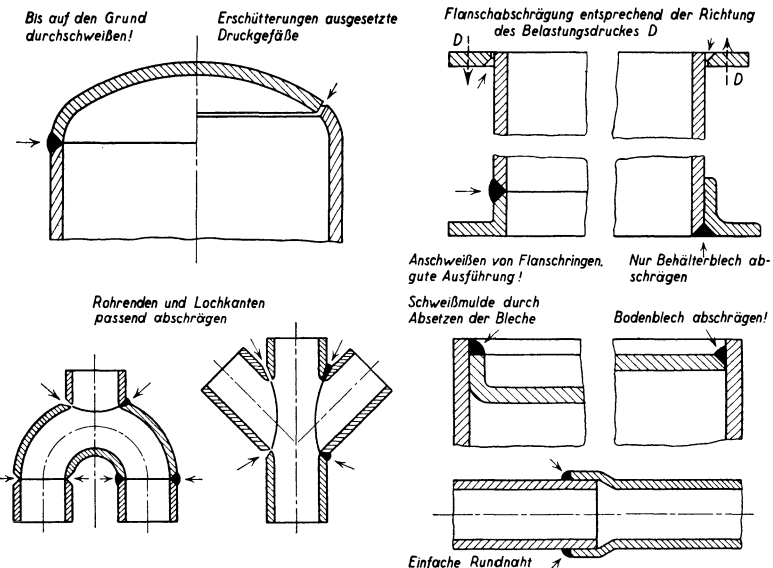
Rohrverbindungen durch Schweißen.
